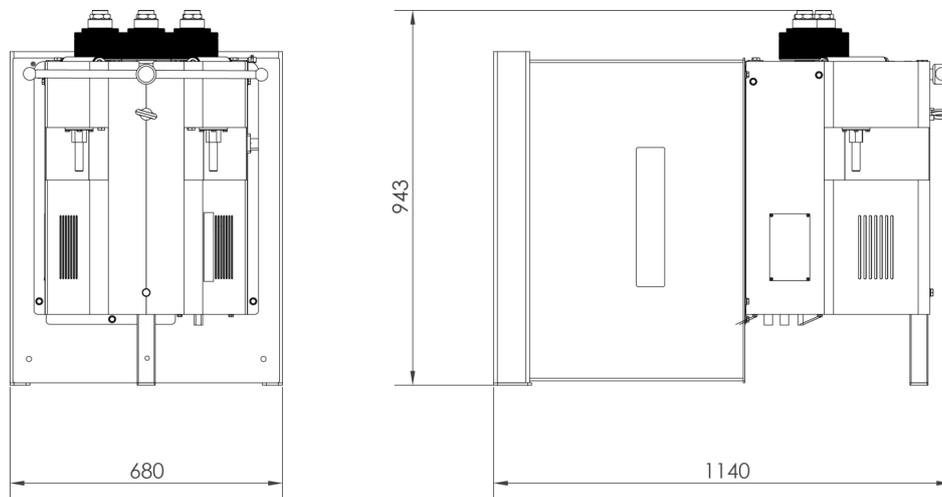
Dimensions de la machine avec le bâti en position horizontale
